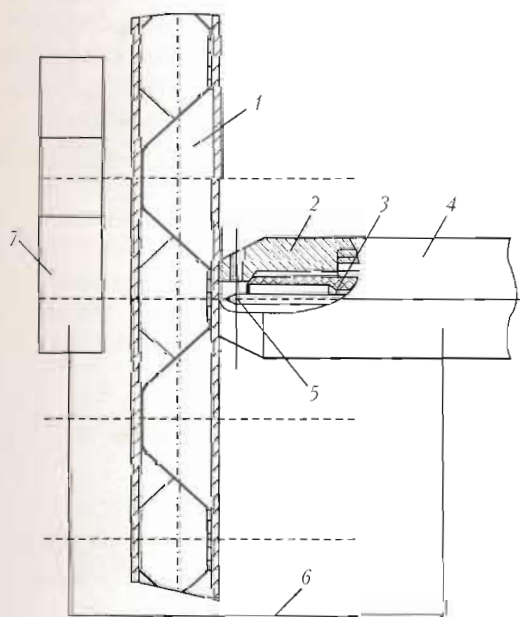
Схема выполнения ДТС трехслойной панели: 1 — трехслойная панель; 2 — опорное сопло; 3 — керамическая вставка; 4 — сварочная горелка; 5 — неплавящийся электрод; 6 — жесткая связь; 7 — система слежения
